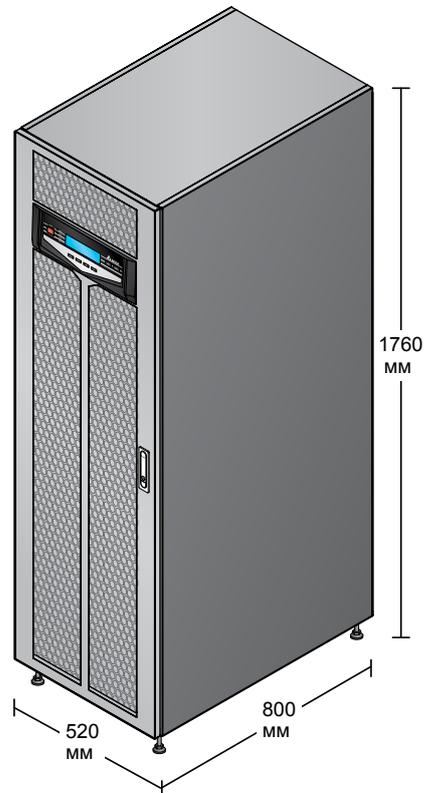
Внешний вид и размеры ИБП 100/120 кВА
